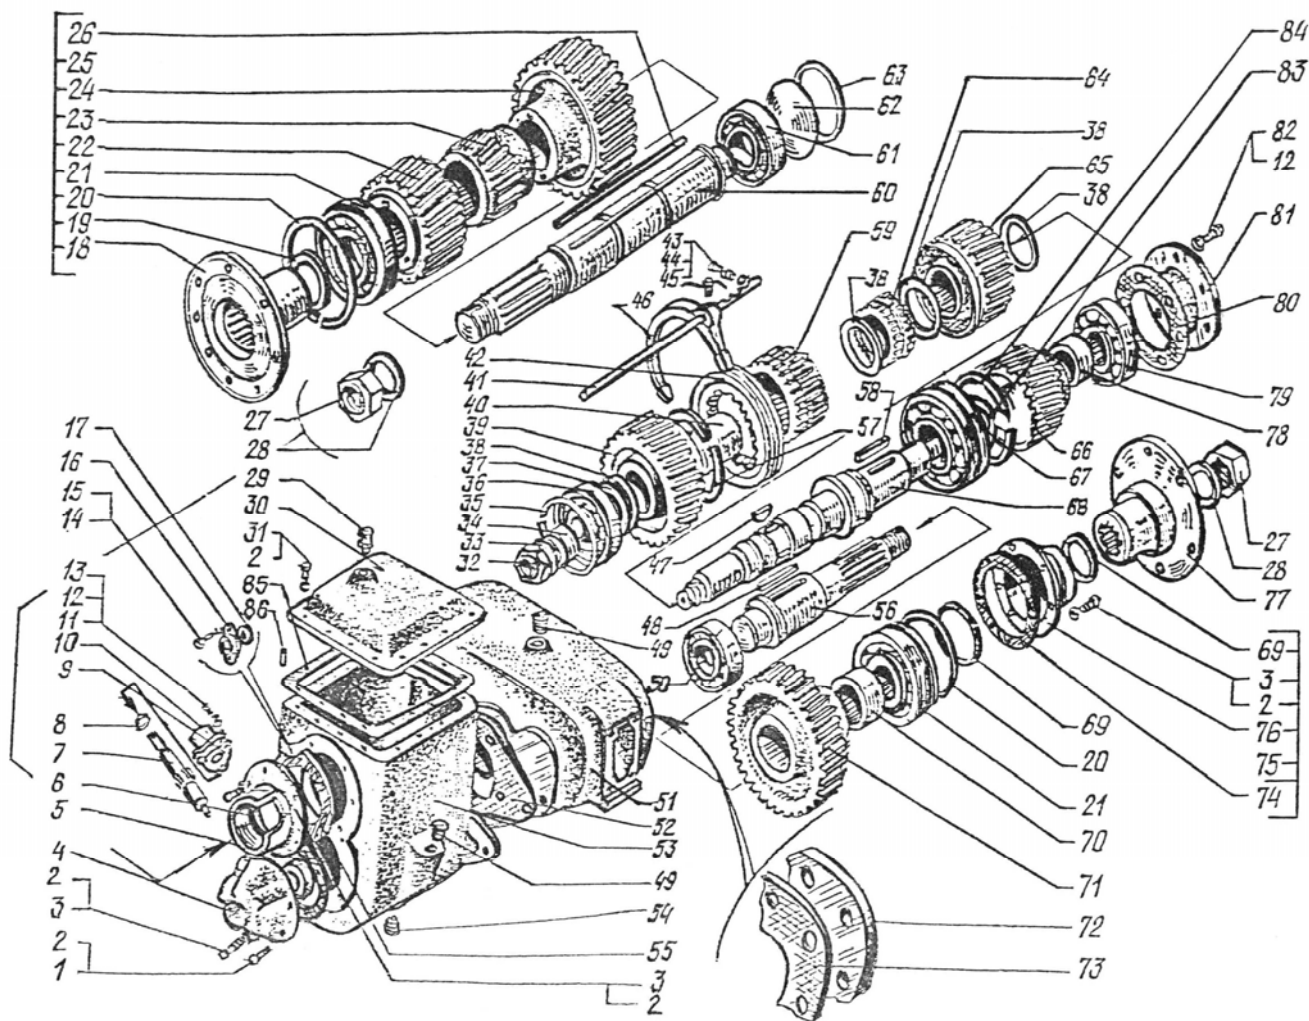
Промежуточная опора – двухступенчатый редуктор:
